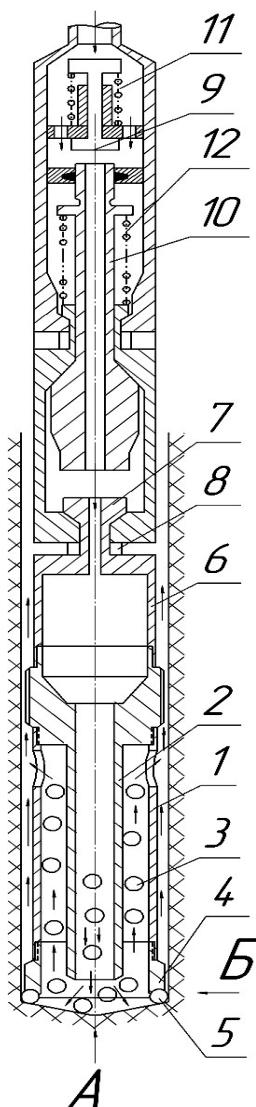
Общая схема шароструйного снаряда с гидроударным приводом
